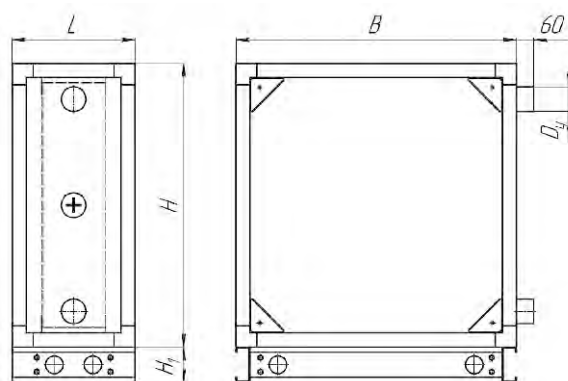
Габаритные размеры. Блок воздунагревателя водяного.
